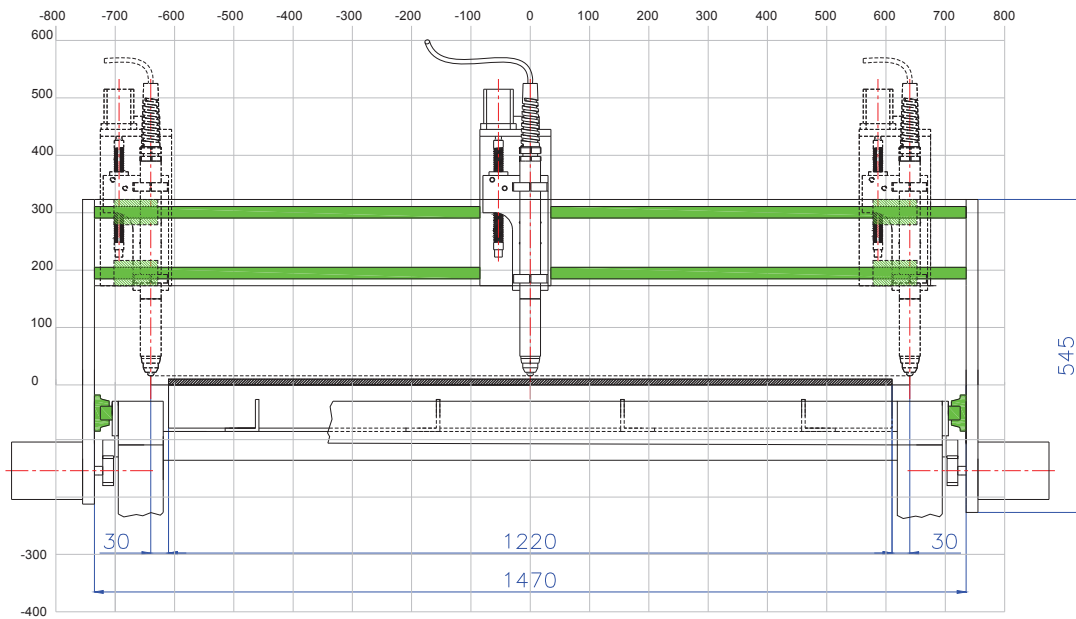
Dimensionamiento EJE Y, vista frontal
